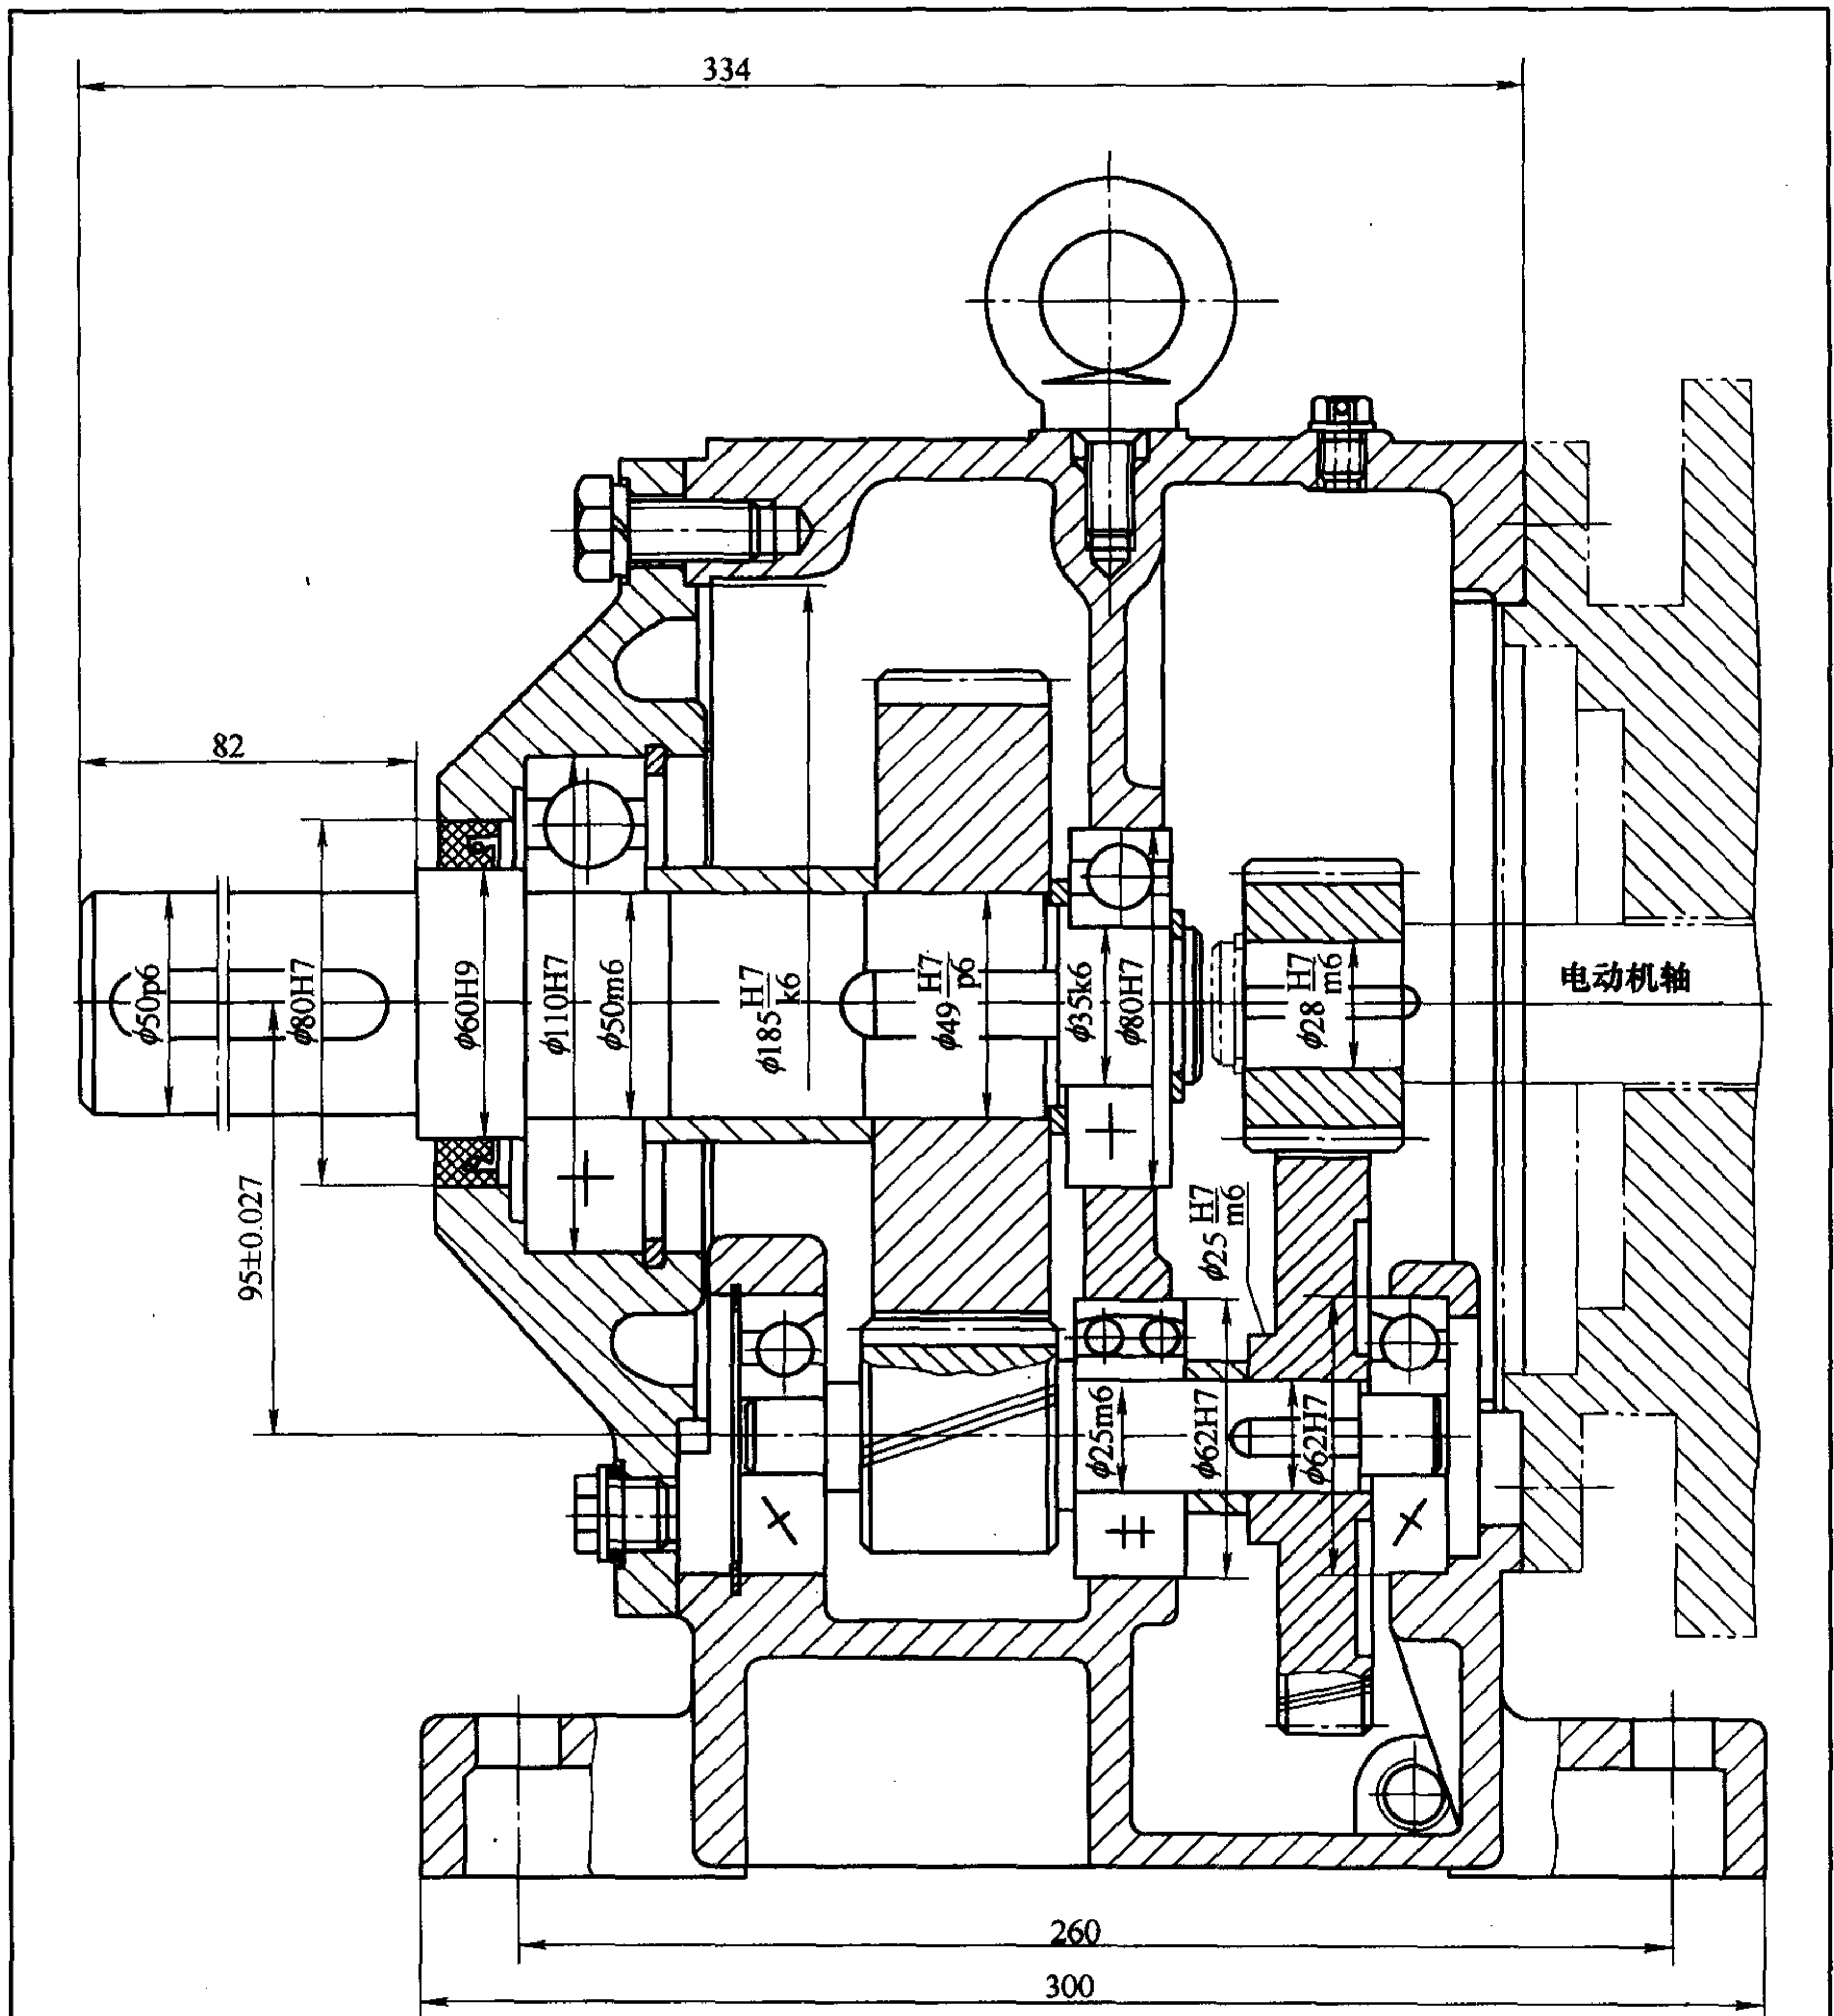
17 二级圆柱齿轮减速器结构图(同轴式套装轴承)
